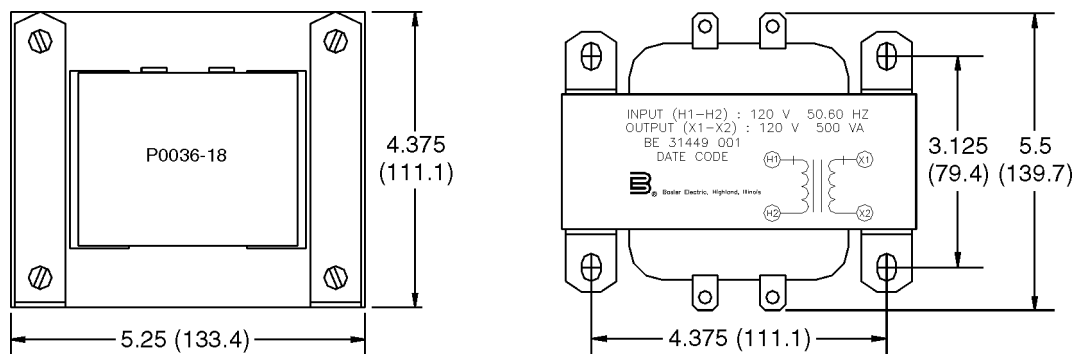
Dimensiones del transformador de aislamiento (BE31449001)
